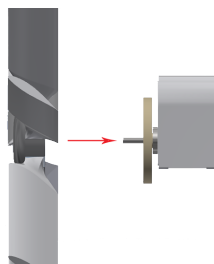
Exploderad vy av prototypens rotor med växellåda avbildad från sidan.
